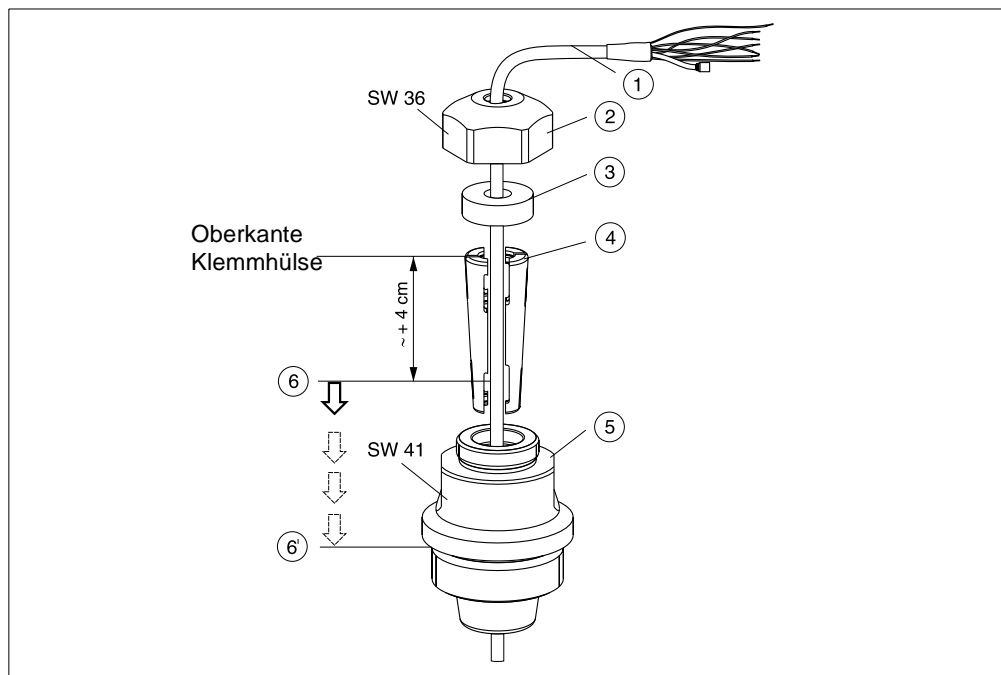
Montage Pegelsonde LGC mit Tragkabel-Montageschraube, hier dargestellt mit Gewinde G1½
